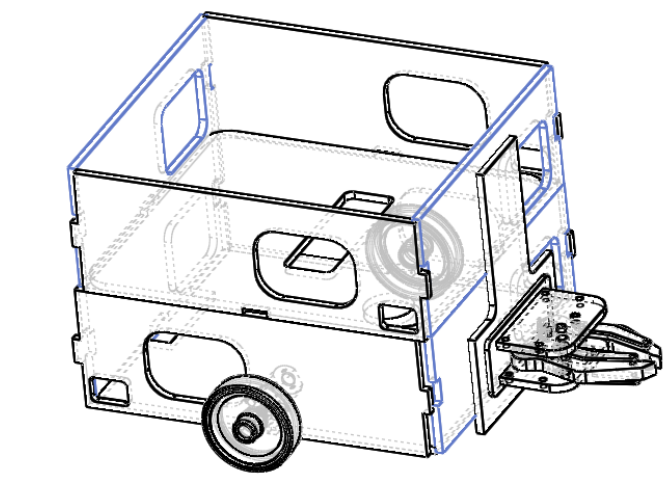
Ensamble en Solidworks de robot recolector de objetos
